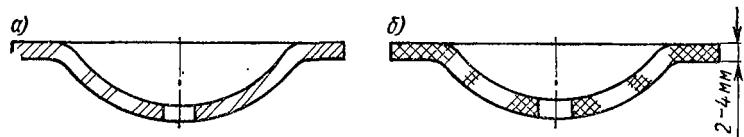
Штриховка узких площадей сечений штампованных и других деталей: а — металлических; б — неметаллических
